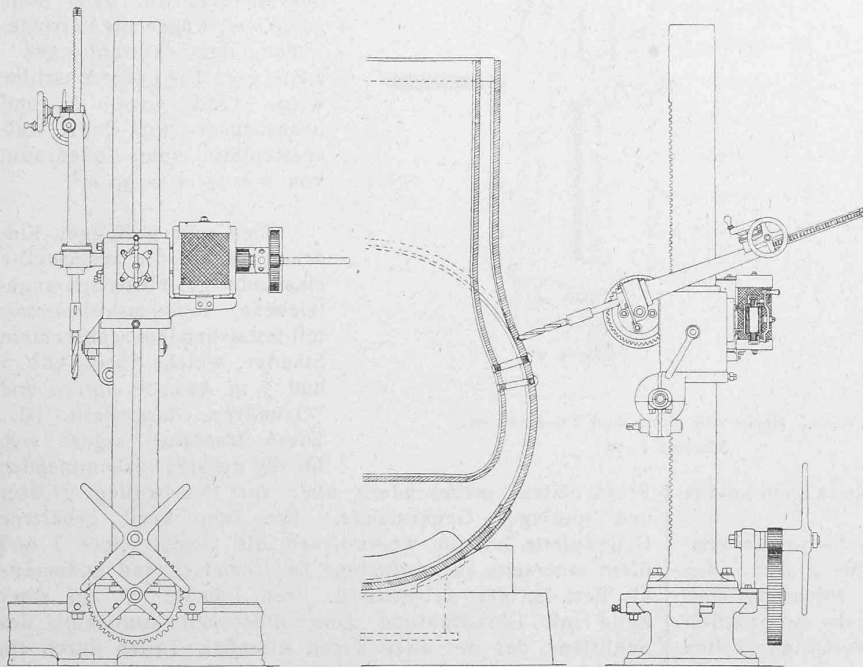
Universal-Bohr- und Gewindeschneidemaschine mit elektr. Antrieb. — Masstab 1 : 30.
